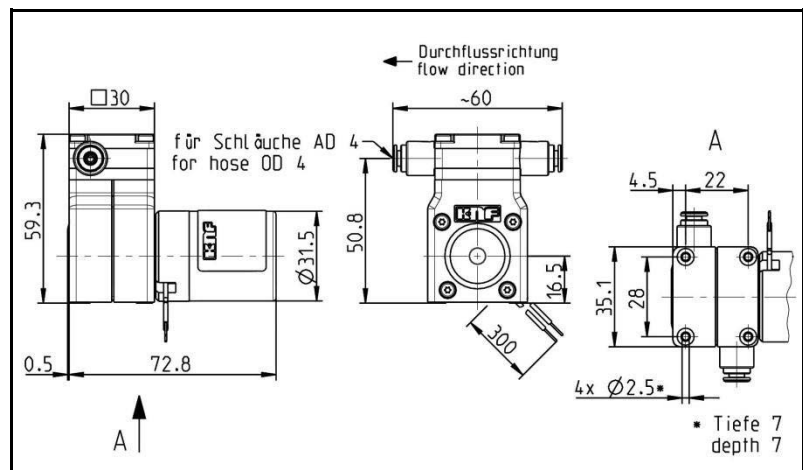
Befestigungsmasse NF 2.35 DCB-A
